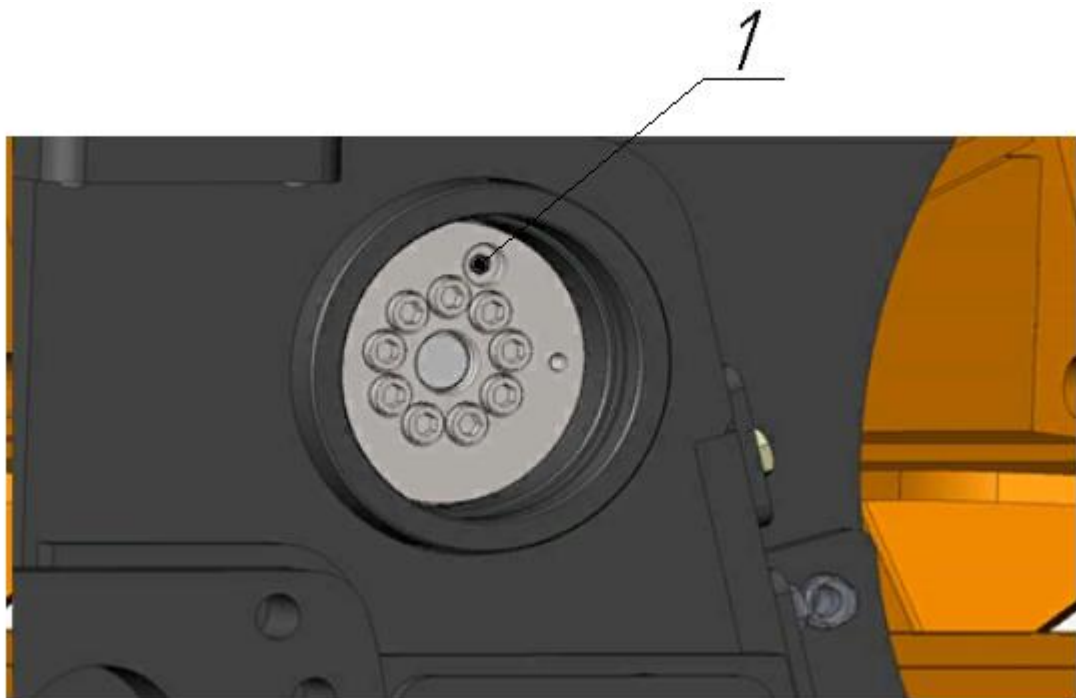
Пресс-масленка для накачки смазки в полуось
